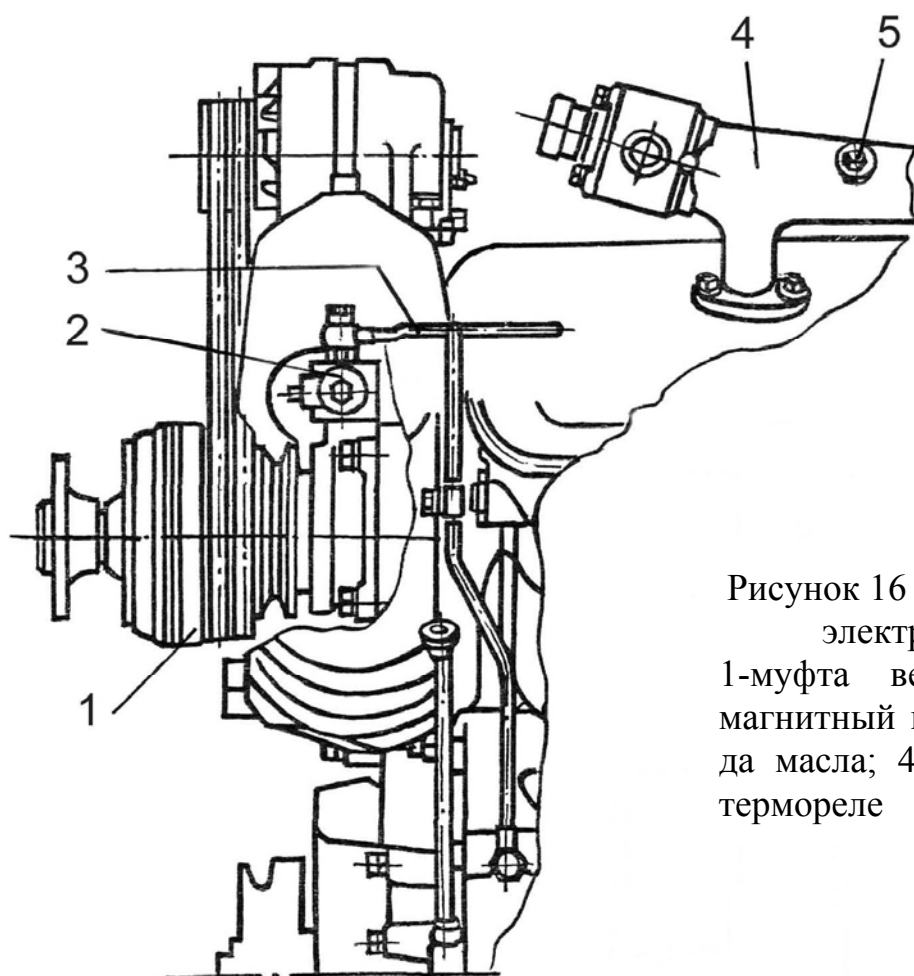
Привод вентилятора с электромагнитным клапаном: 1-муфта вентилятора; 2-электромагнитный клапан; 3-трубка подвода масла; 4-водяной коллектор; 5-термореле
